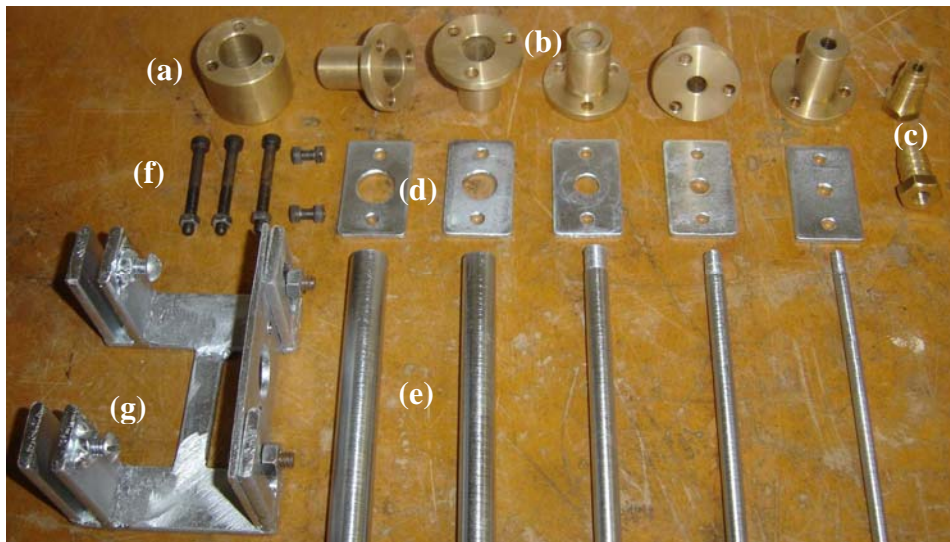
Elementos metálicos: (a) bucha de bronze; (b) flanges de bronze; (c) adaptadores de bronze; (d) chapas de aço; (e) tubos de aço carbono; (f) parafusos; (g) suporte móvel de aço.
